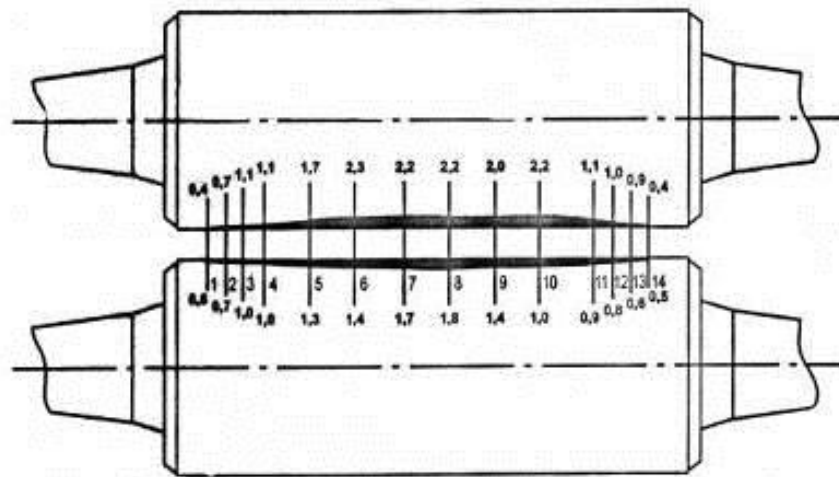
Зношення (мм) робочої поверхні валка
